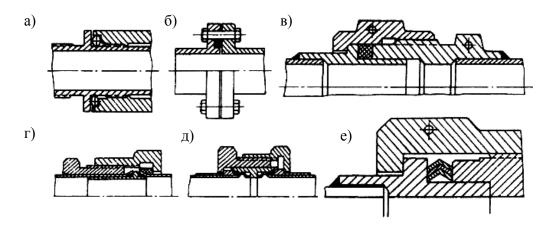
Схемы разъемных неподвижных фланцевых соединений трубопроводов с уплотнительными прокладками: а – с трубчатыми кольцевыми уплотнениями; б – с резиновыми кольцами; в – с прямоугольными гнездами; г, д – с клиновыми гнездами; е – с упругими пластинчатыми элементами
